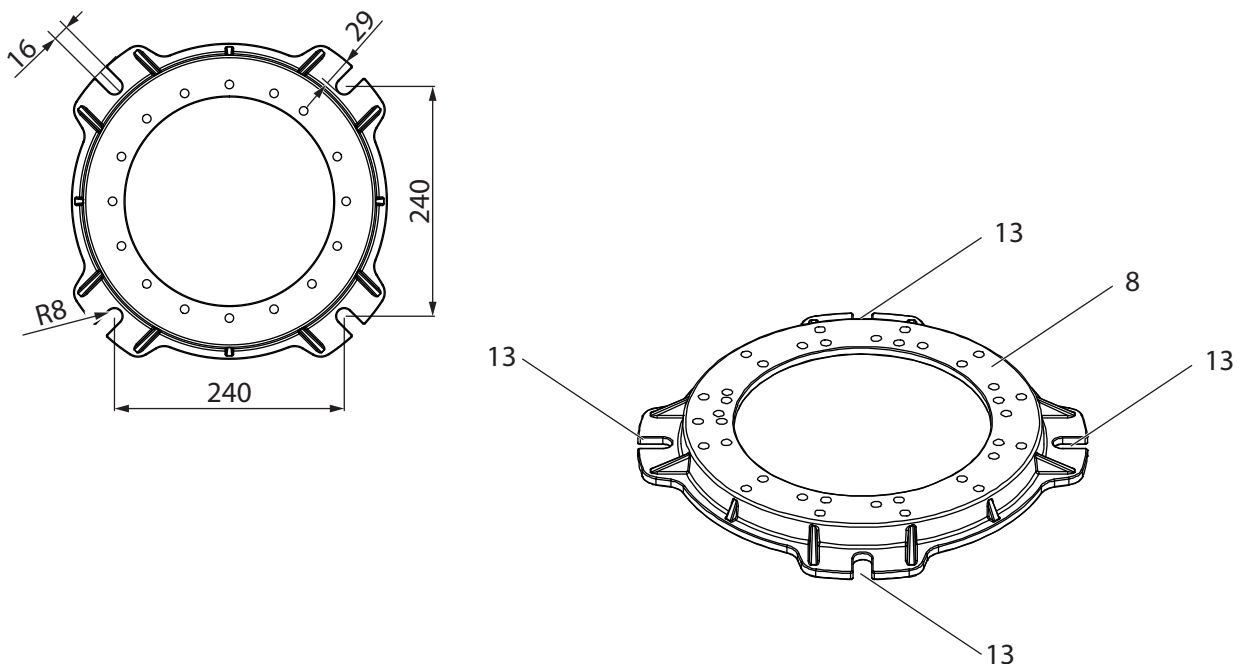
Mechanische Montage – Befestigungsfuß – Beispiel (Maße in mm)
